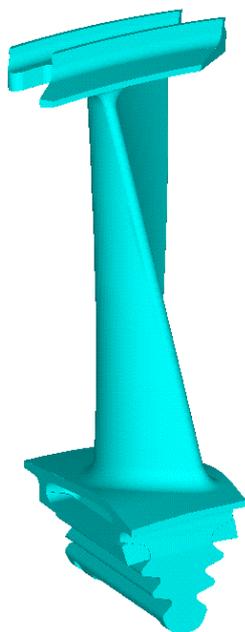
Рабочая лопатка свободной турбины малоразмерного АГТД
